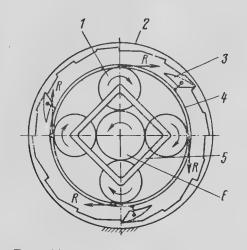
Схема работы муфты сцепления-расцепления: 1 — сателлитовое колесо; 2 — храповое колесо; 3 — «собачки»; 4 — зуб-
